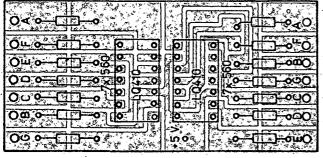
Obrazec plošných spojů desky zesilovače a zdroje T121
